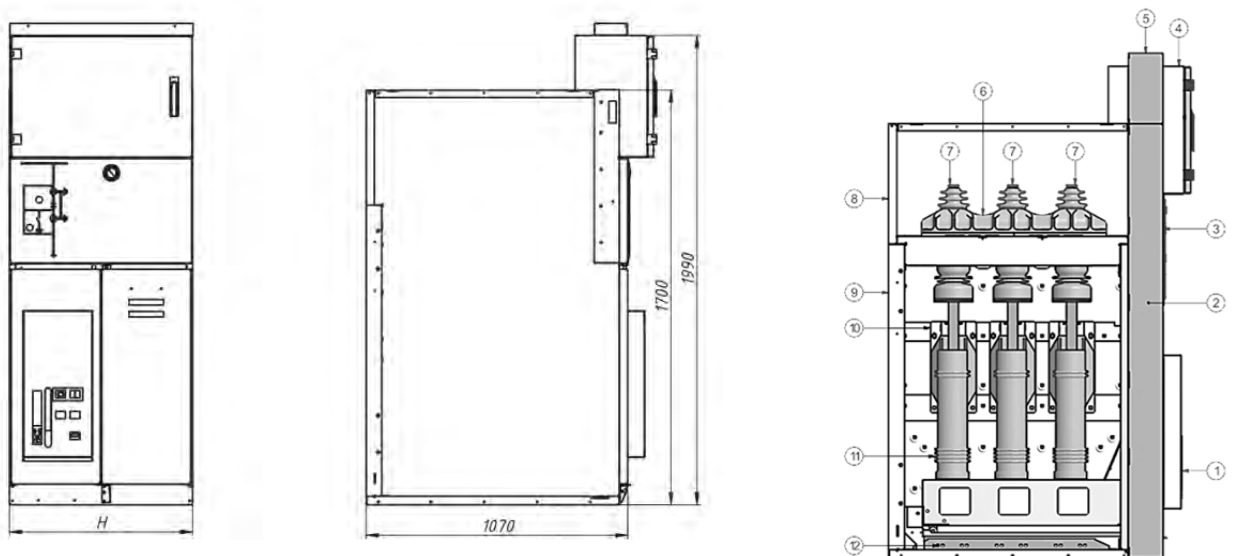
Конструктив и габаритные размеры камеры КСО2-20
